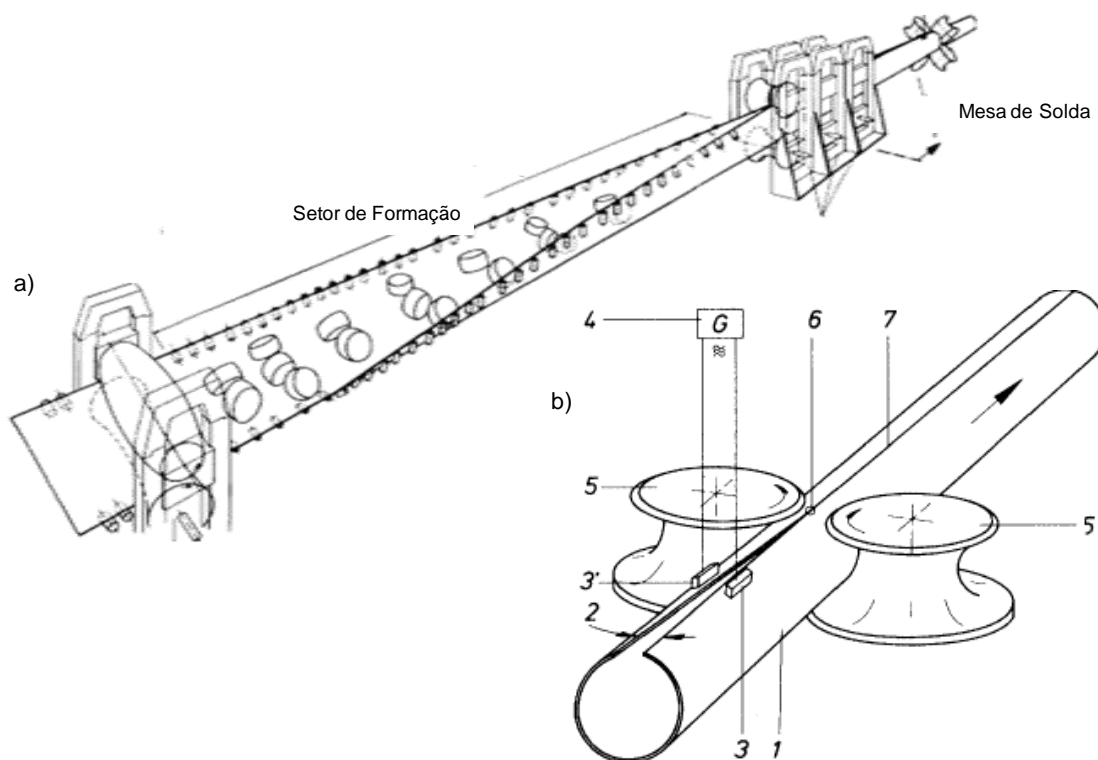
Processo de formação e solda ERW. a) conformação da bobina por rolos até o formado tubular; b) detalhamento do processo de solda por eletrodos de contato: 1) tubo sem solda; 2) abertura inicial antes da soldagem; 3) eletrodos de contato; 4) transformador; 5) rolos de aperto; 6) ponto de soldagem; 7) cordão de solda. Adaptado de [36].
